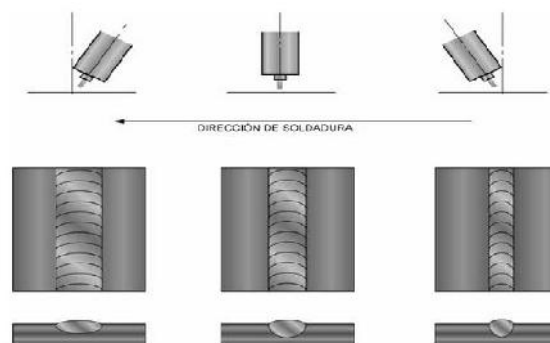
8: Orientación del alambre de soldadura.
